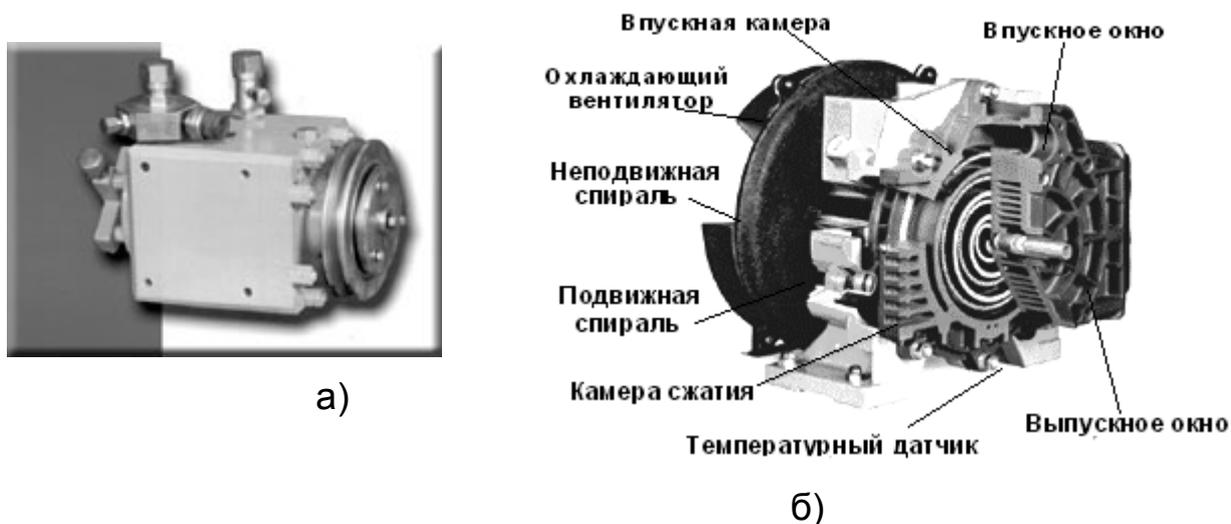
25. Внешний вид (а) и разрез (б) спирального компрессора
